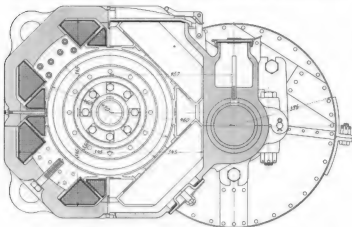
Bahnmotor mit Wendepolen. Siemens-Schuckertwerke. Maßstab 1:10.
